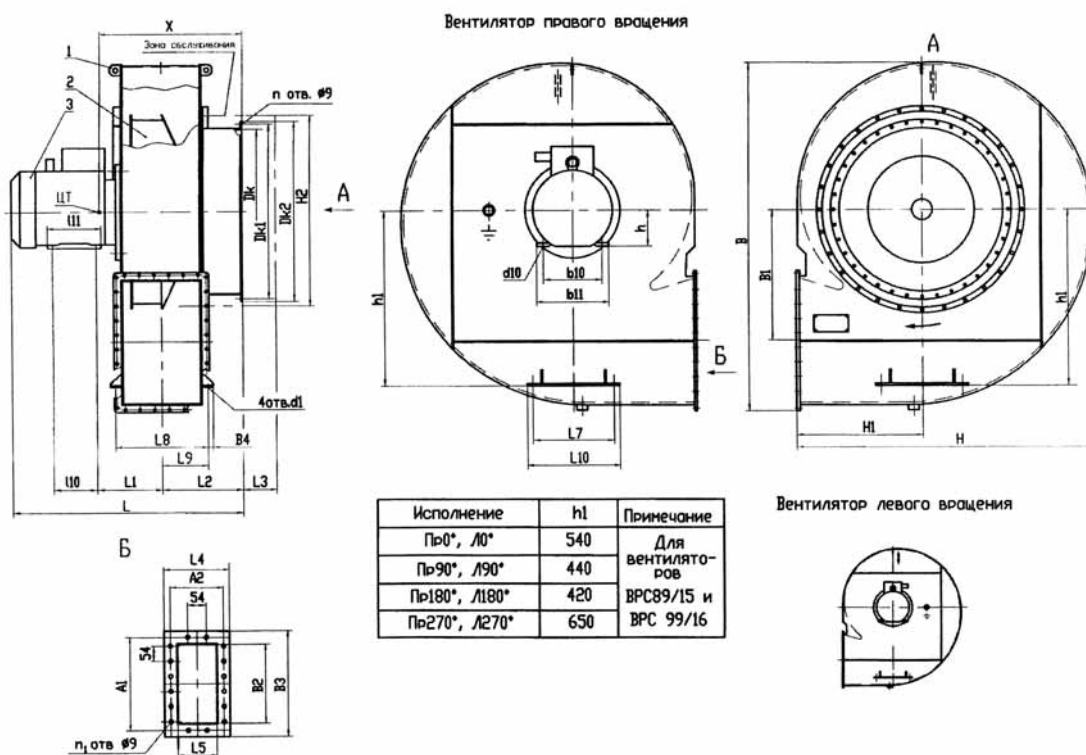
1 – корпус; 2 – колесо; 3 – двигатель
